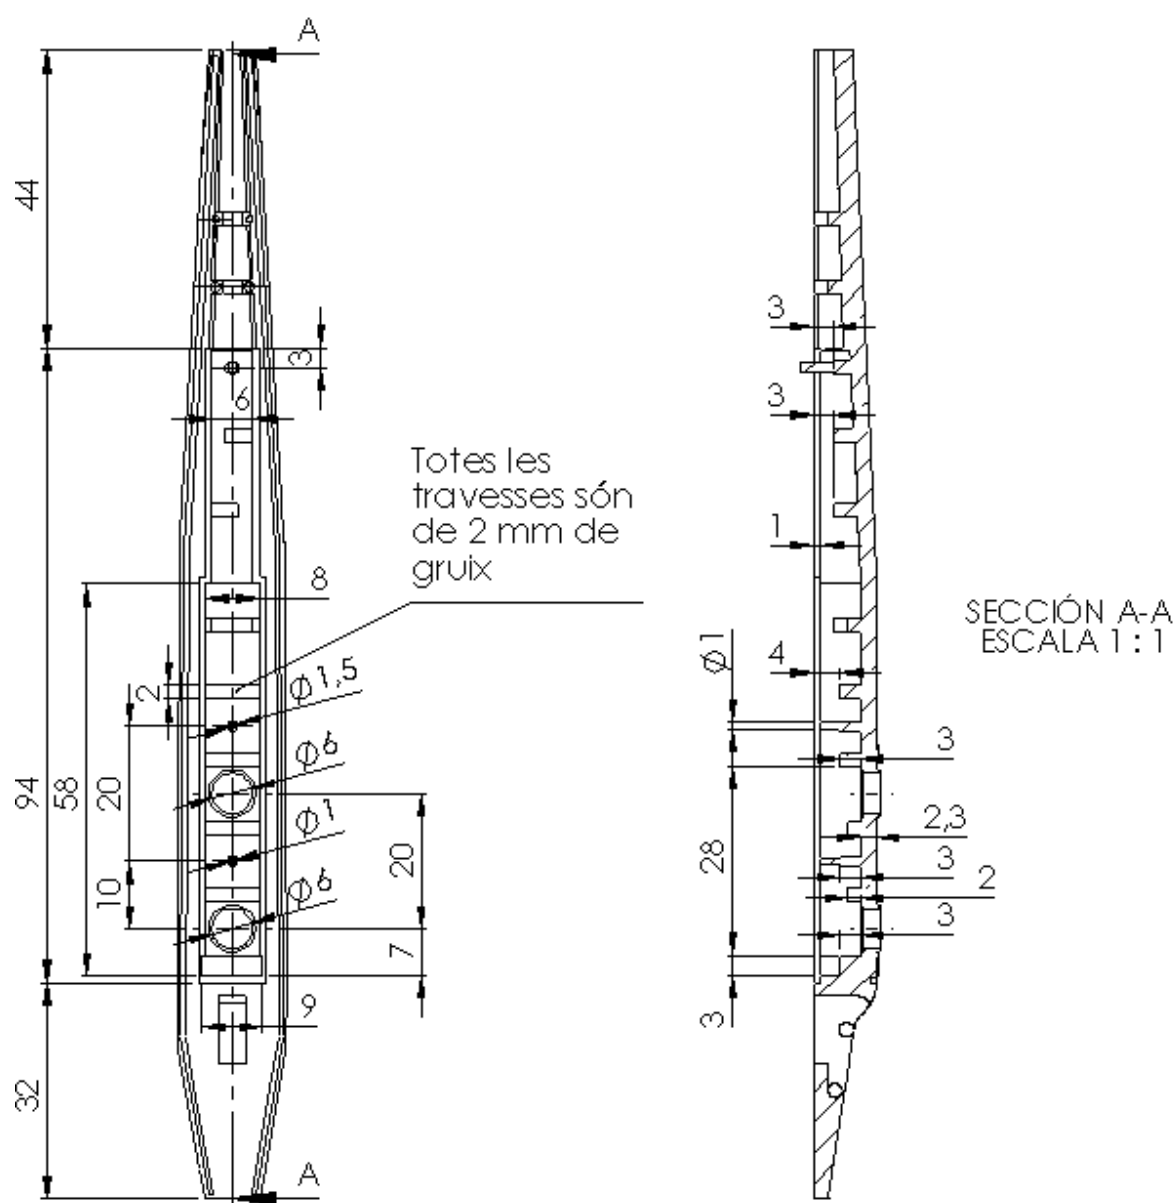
Carcassa superior. 3er Muntatge. Vista de planta (figura de l'esquerra) i secció de la vista de planta (figura de la dreta, secció A-A).
